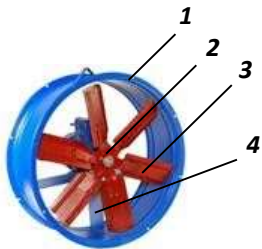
Осевий вентилятор: 1 – корпус; 2 – робоче колесо; 3 – лопатки; 4 – рама
